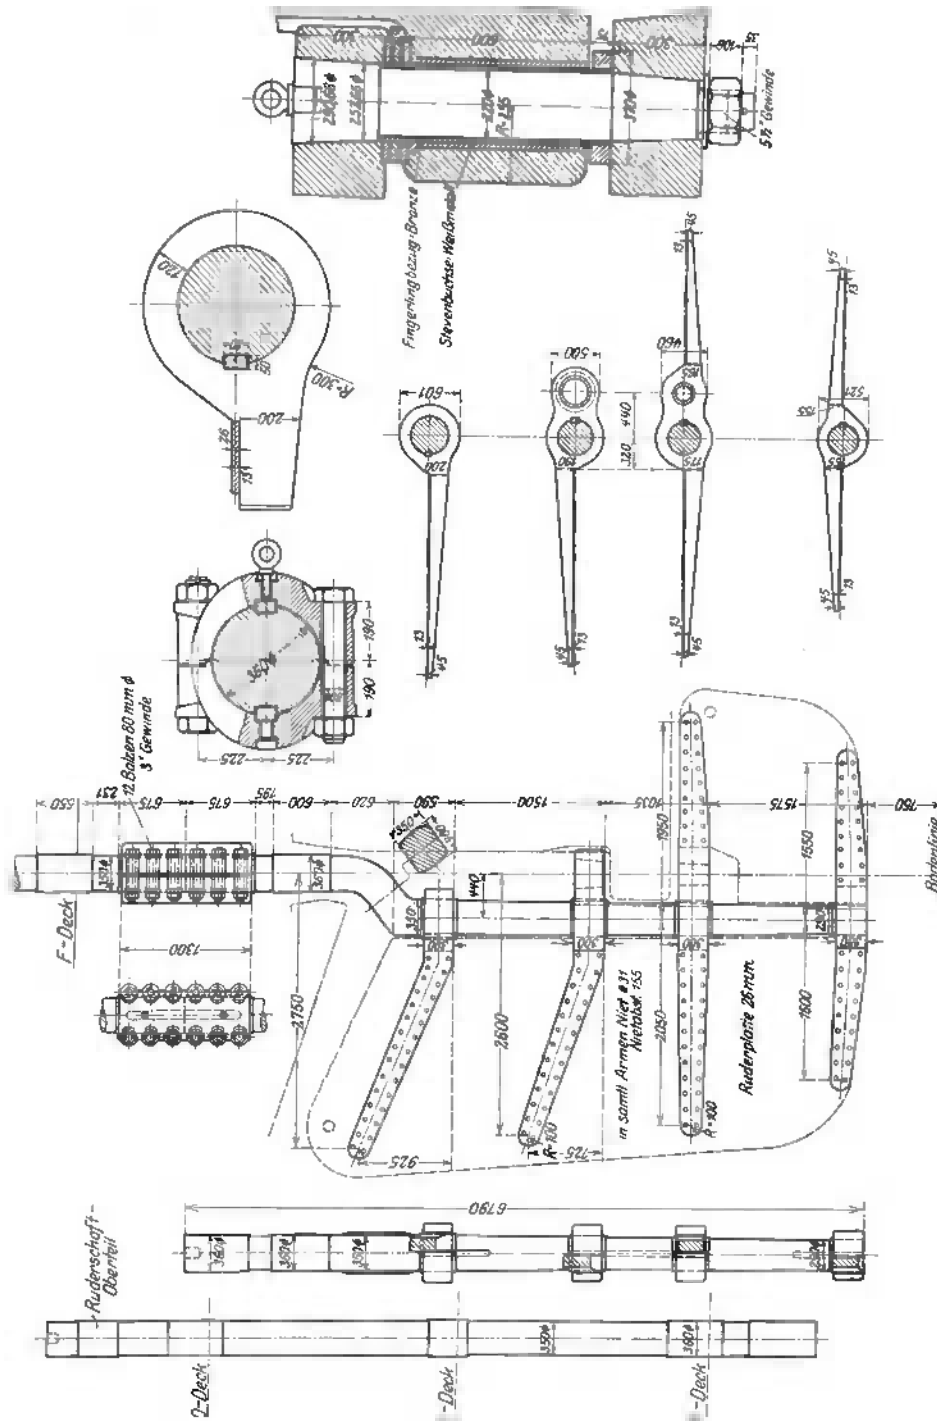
Ruder des Zweischraubenmotorschiffes „Monte Sarmiento“.
